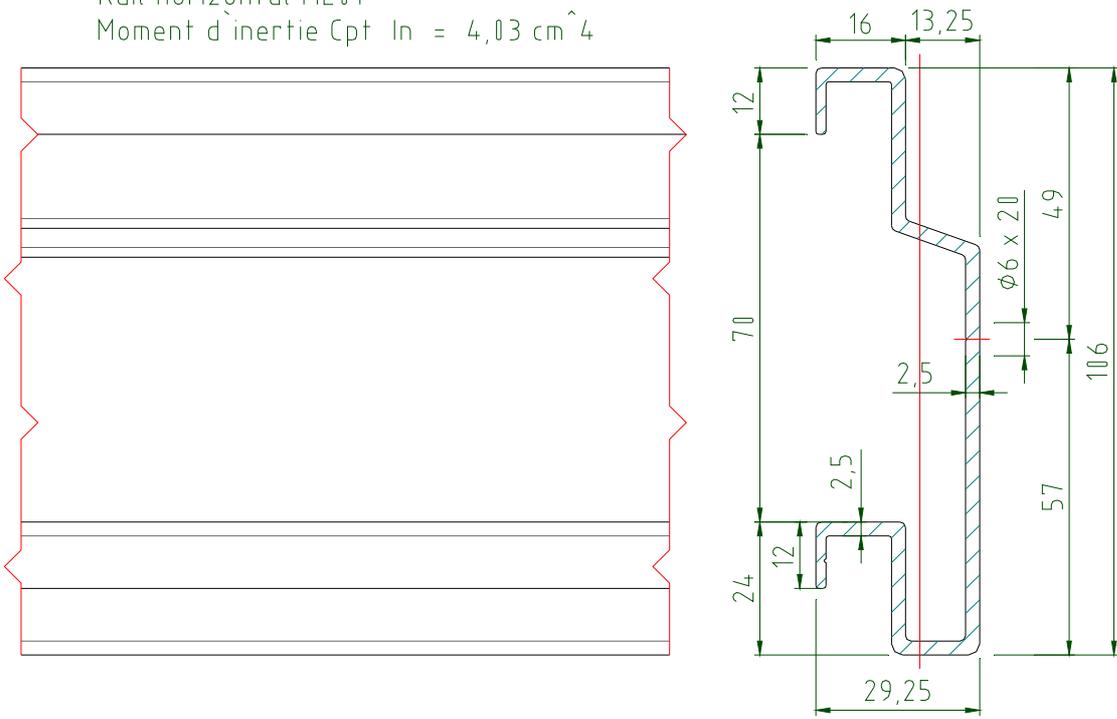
Rail horizontal aluminium épaisseur 2,5 mm (longueur maxi 3 m)
